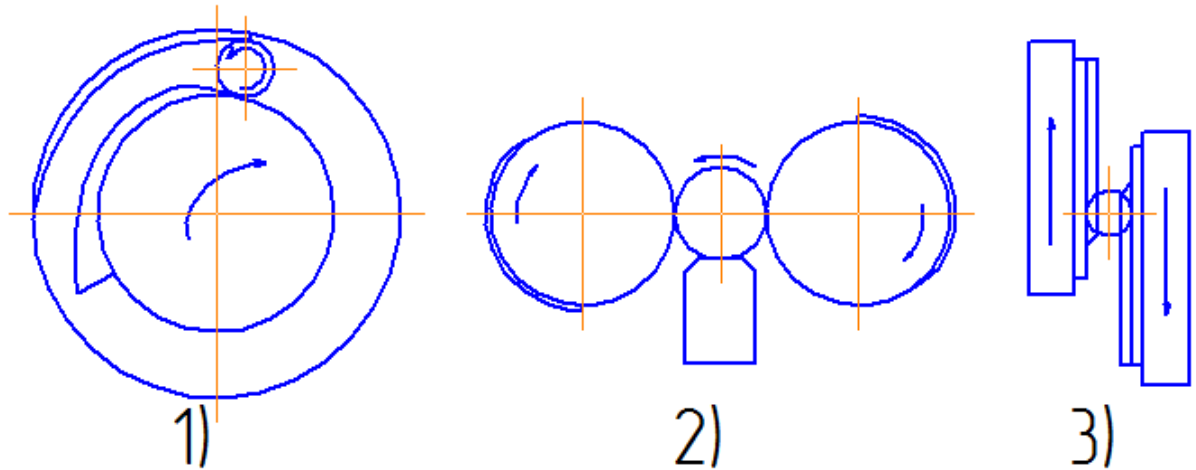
Схема поперечно-клиновой вальцовки:
